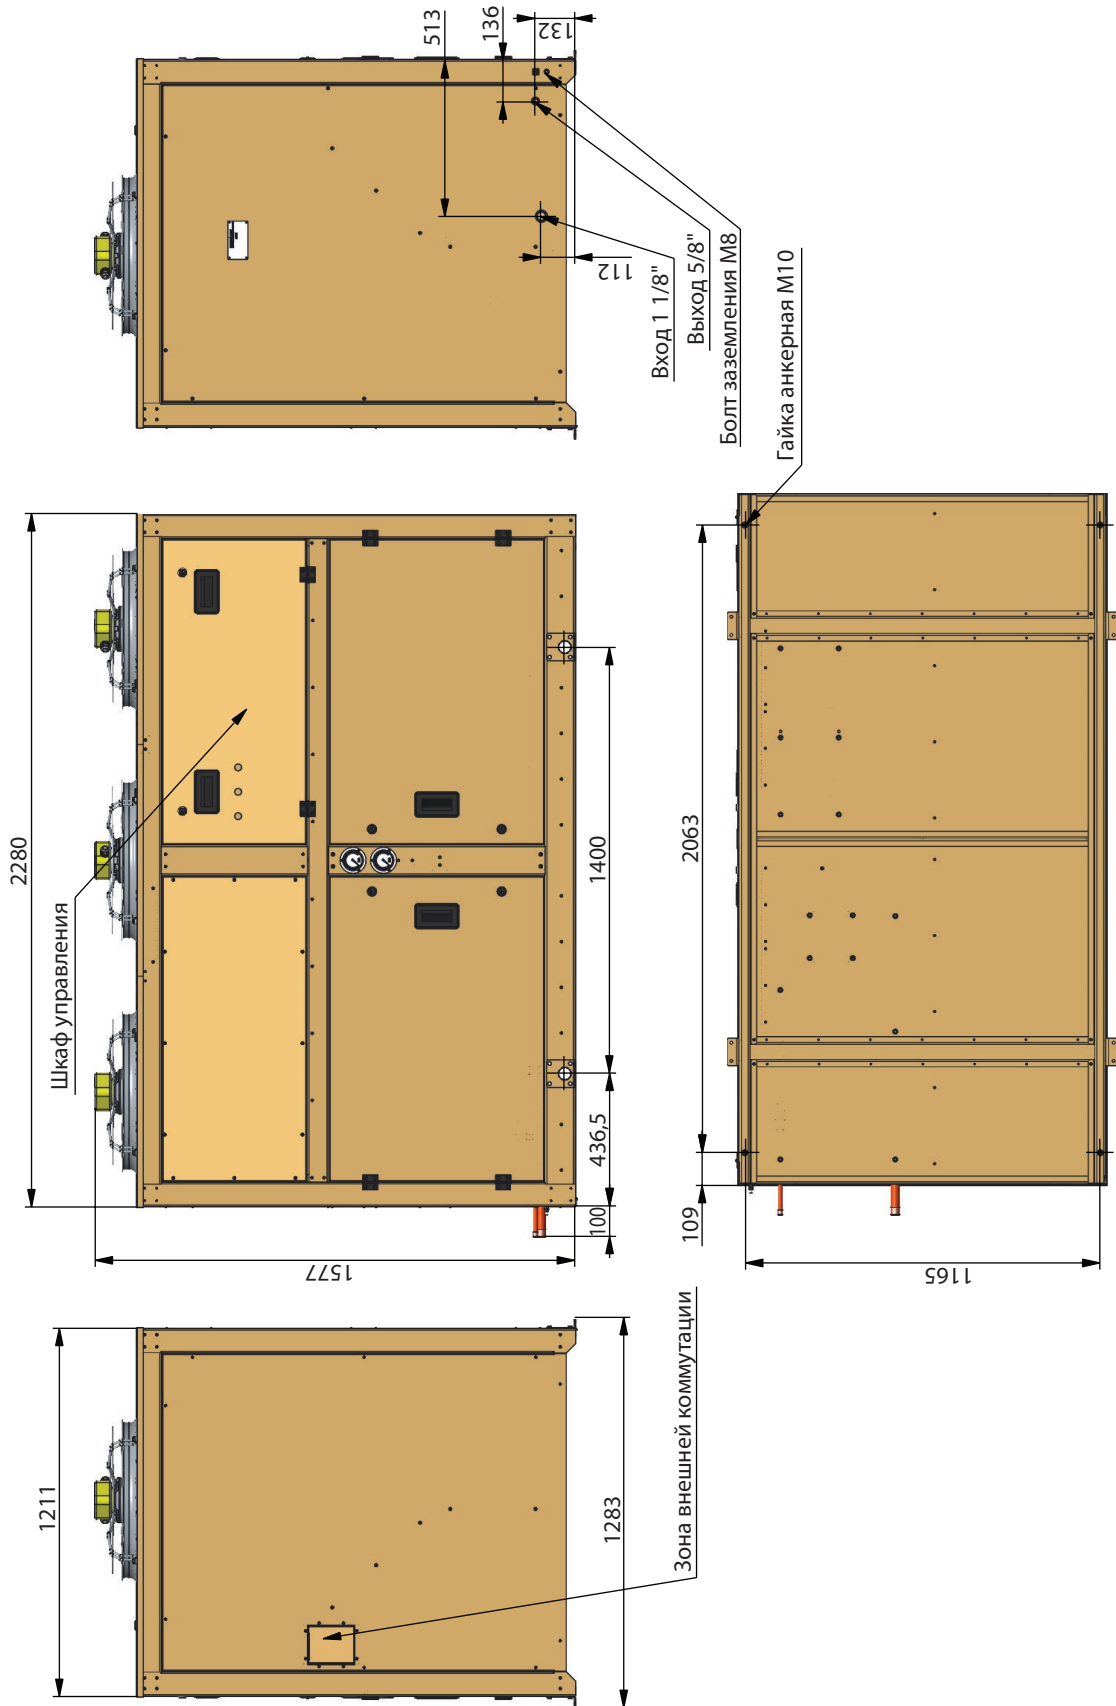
Агрегат компрессорный типа МАКК 320-401, -451
